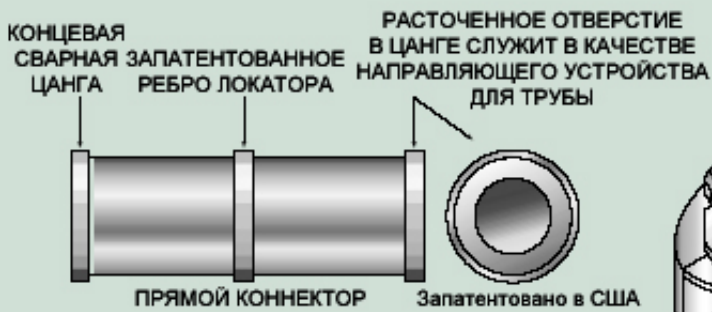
Фитинг с автоматической стыковой сваркой обладает ребром локатора, расположенным на фиксированном расстоянии от конца сварной цанги
